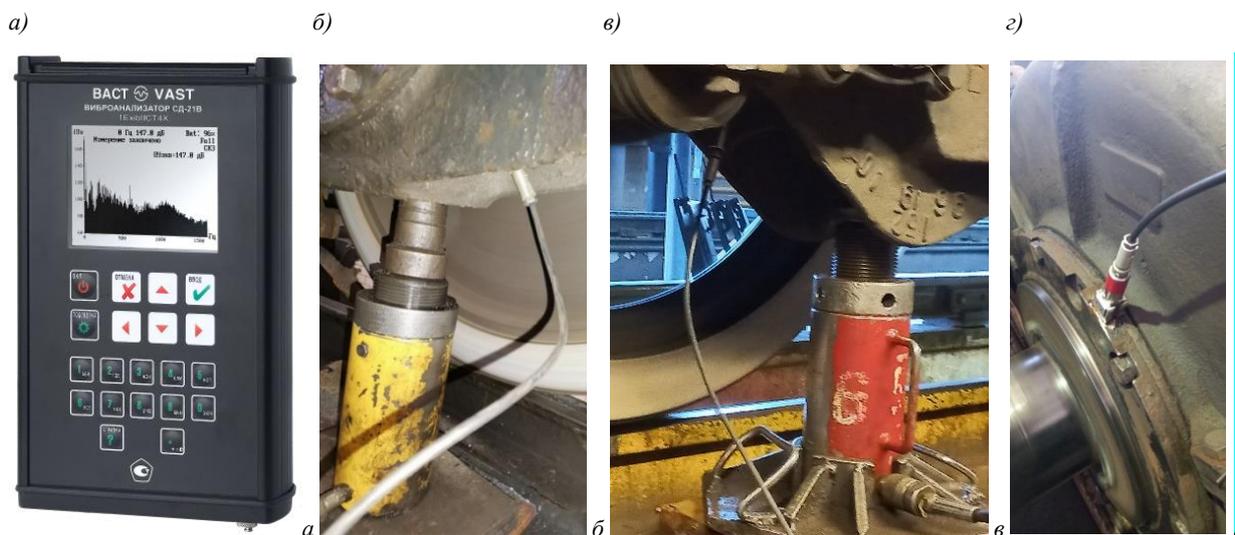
Пример проведения ВД подшипников буксового узла
